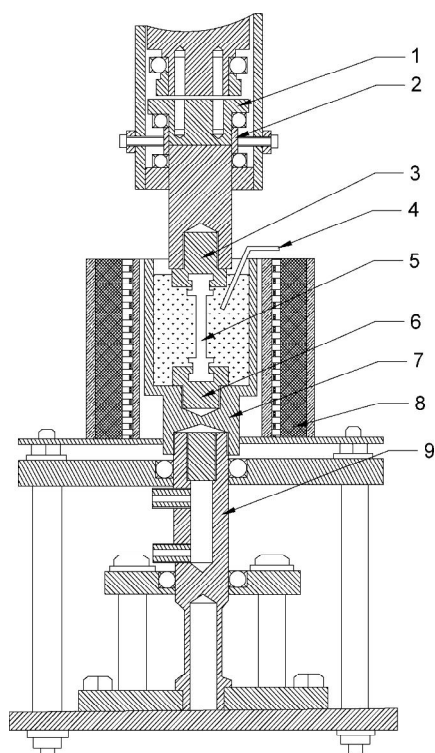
Схема установки для испытаний на горячее скручивание с нагревом в расплаве солей: 1–электромагнитная муфта; 2–тормозные колодки; 3–активный захват; 4–система продувки; 5–образец для скручивания; 6–пассивный захват; 7–стакан; 8–печь; 9–вал с водяным охлаждением
